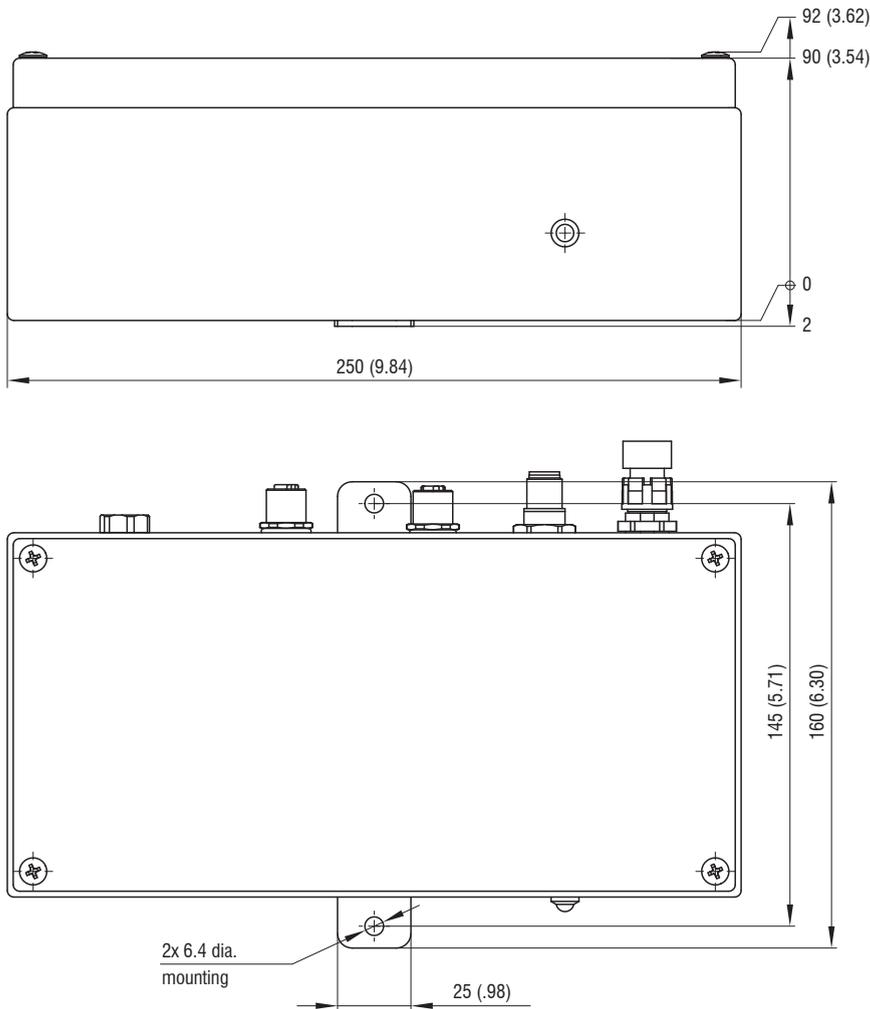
Maßzeichnung Front- und Draufsicht des Controllers IMC5420IP67, Abmessungen in mm (Zoll)
